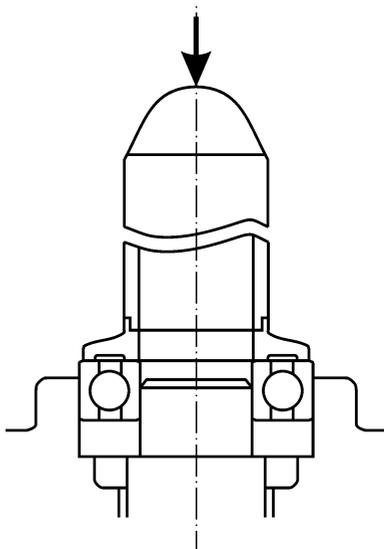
Передача усилий монтажа на оба кольца подшипника
